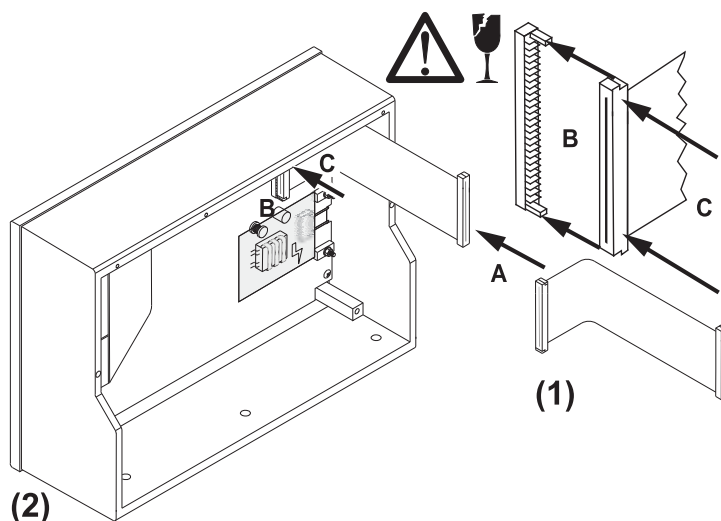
Aufstecken des Flachband-Anschlusskabels auf die Displayplatine
